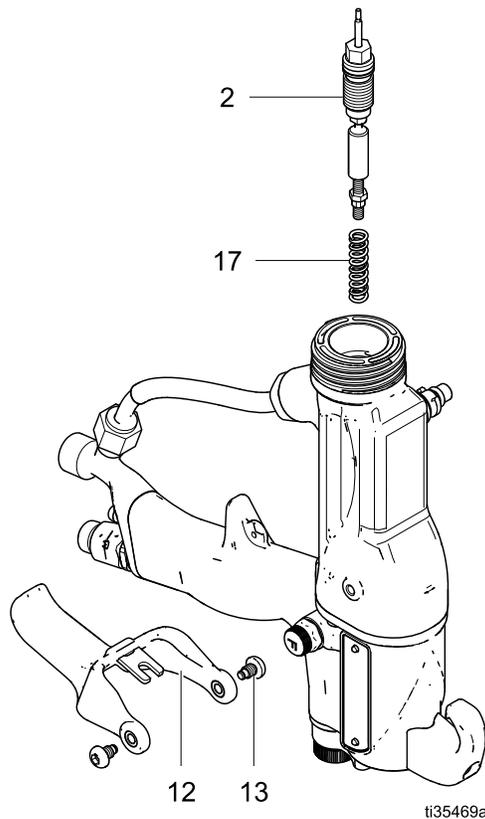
Desmontaje de la varilla de empaquetadura de fluido
